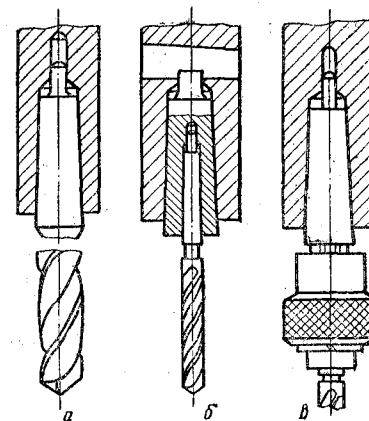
Способы закрепления инструментов в шпинделе сверлильного станка
